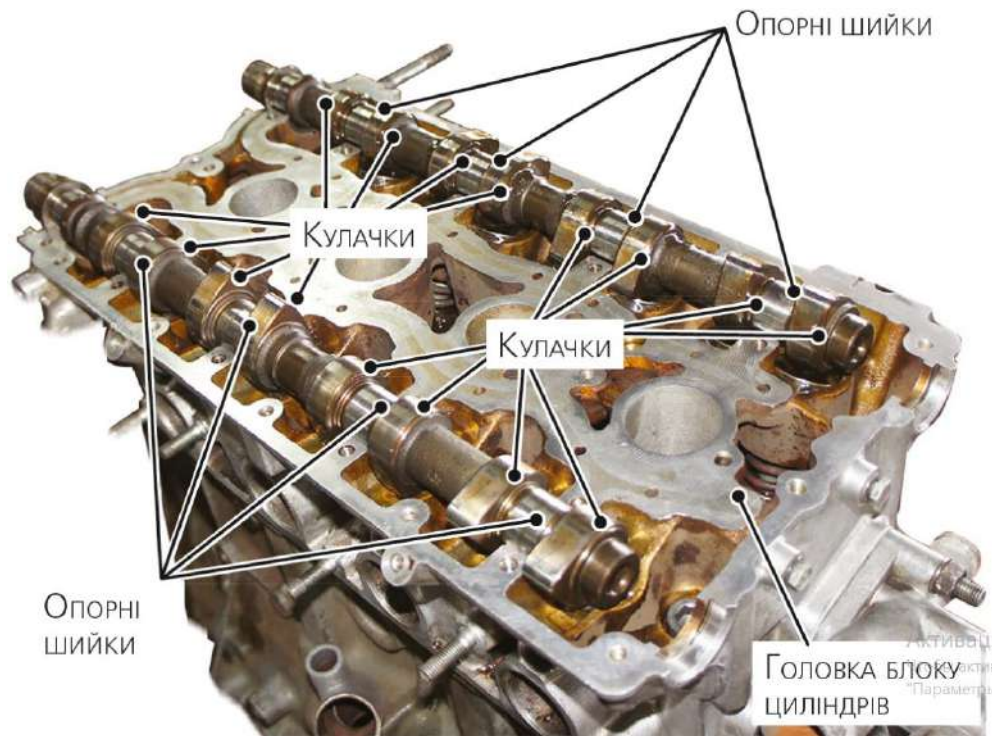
Головка блоку циліндрів з розподільними валами [10]
